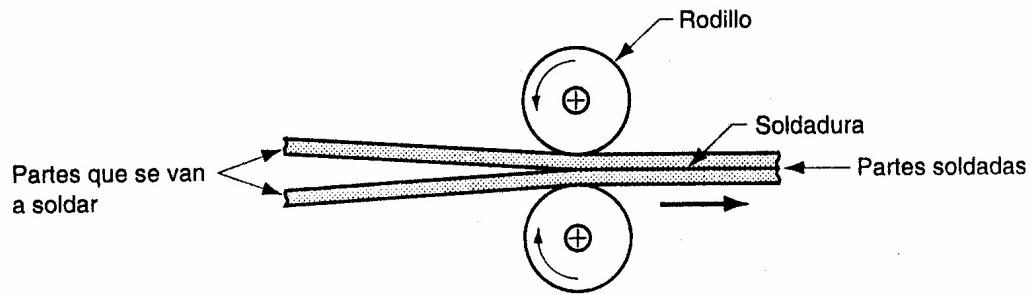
Soldadura con rodillos (ROW).
